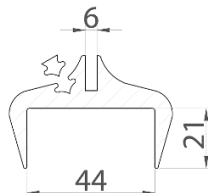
Профиль уплотнительный для обрамления оконных проемов маятниковых дверей
